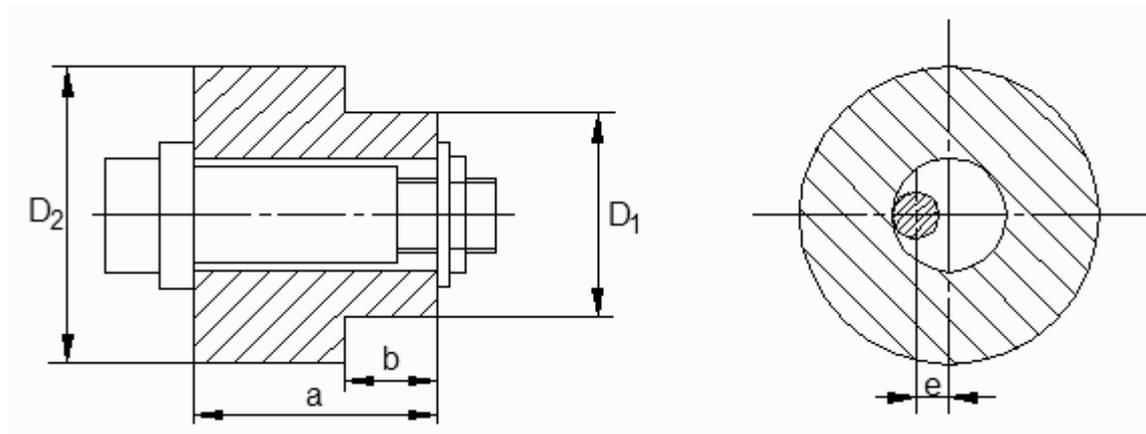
Обработка детали на цилиндрической оправке.
